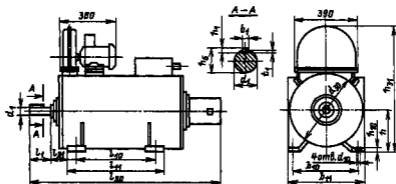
6 Габаритные и установочно-присоединительные размеры ЭМП серии ВД
